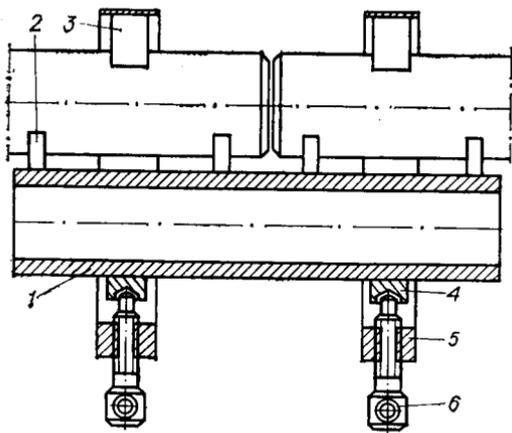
Приспособление для центровки труб при сварке: 1 — основание; 2 — опорная призма; 3 — прижимная призма; 4 — опора для винта; 5 — хомут; 6 — винт.
